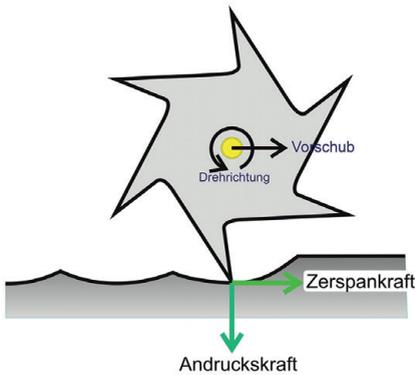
Kräfte, die auf die Schneide eines Fräsers wirken
